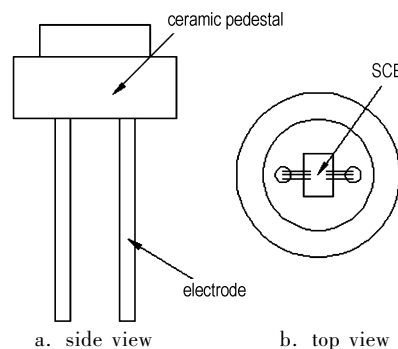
SCB 点火装置结构图 (a) 侧视图 (b) 俯视图
